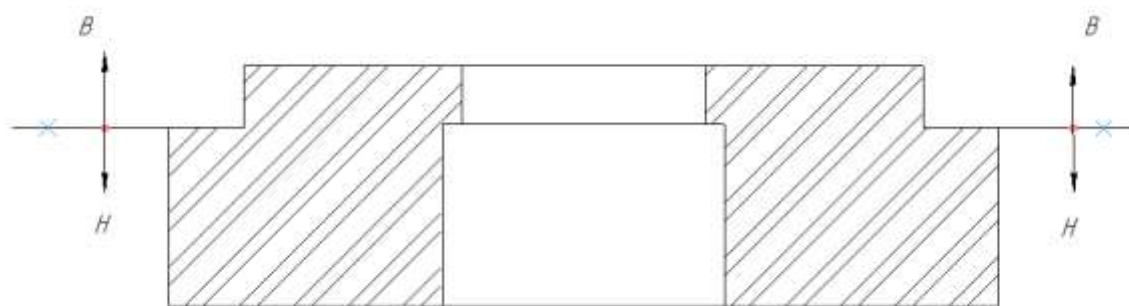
Ескіз заготовки деталі «Кришка пневмоциліндра»
